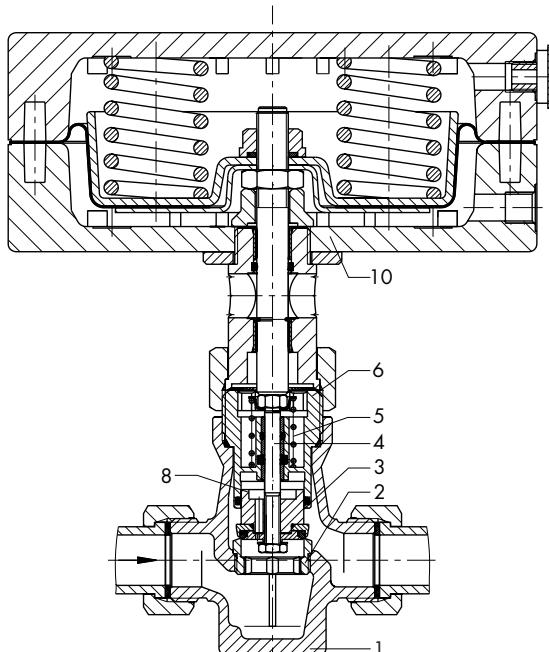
· Organe de réglage pneumatique type 3222/2780-1
